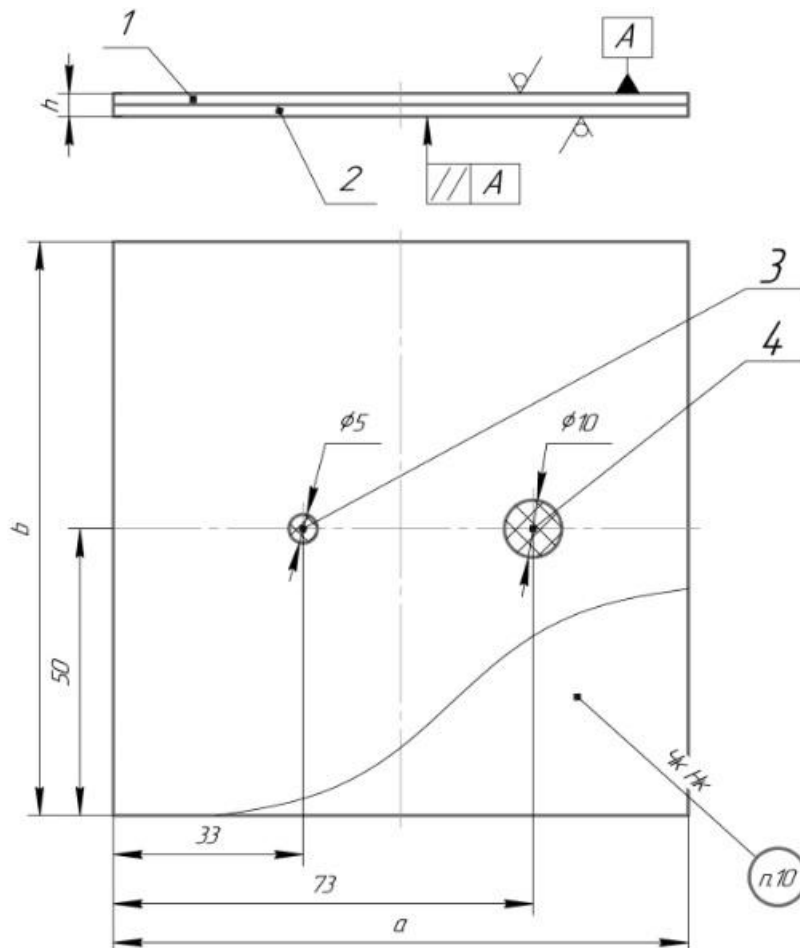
Эскиз образца с координатами расположения имитаторов дефектов
